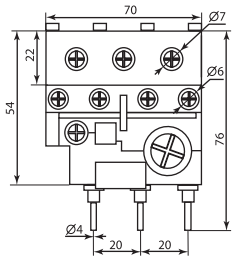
Габаритные и установочные размеры реле PTL-2053-M2...PTL-2066-M2
